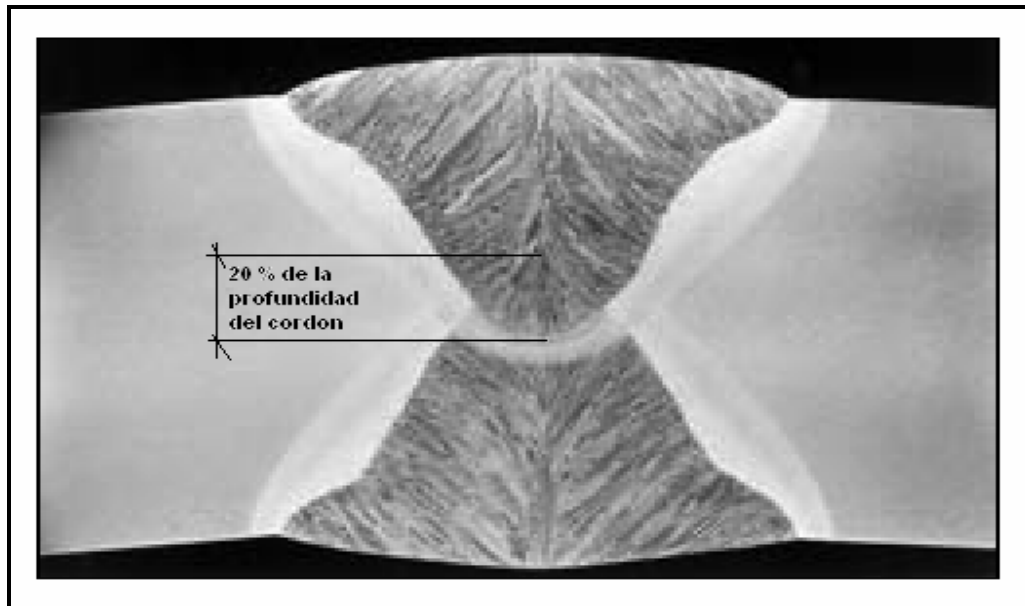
Radiografía de una sección soldada de un tubo helicoidal.
